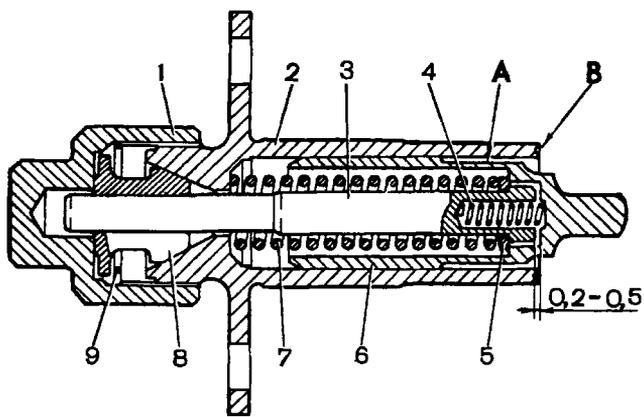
Натяжитель цепи: 1 - колпачковая гайка; 2 - корпус натяжителя; 3 - стержень; 4 - пружина плунжера; 5 - шайба; 6 - плунжер; 7 - пружина; 8 - сухарь; 9 - пужинное кольцо; А - поверхность плунжера; В - места крепления на торце корпуса
